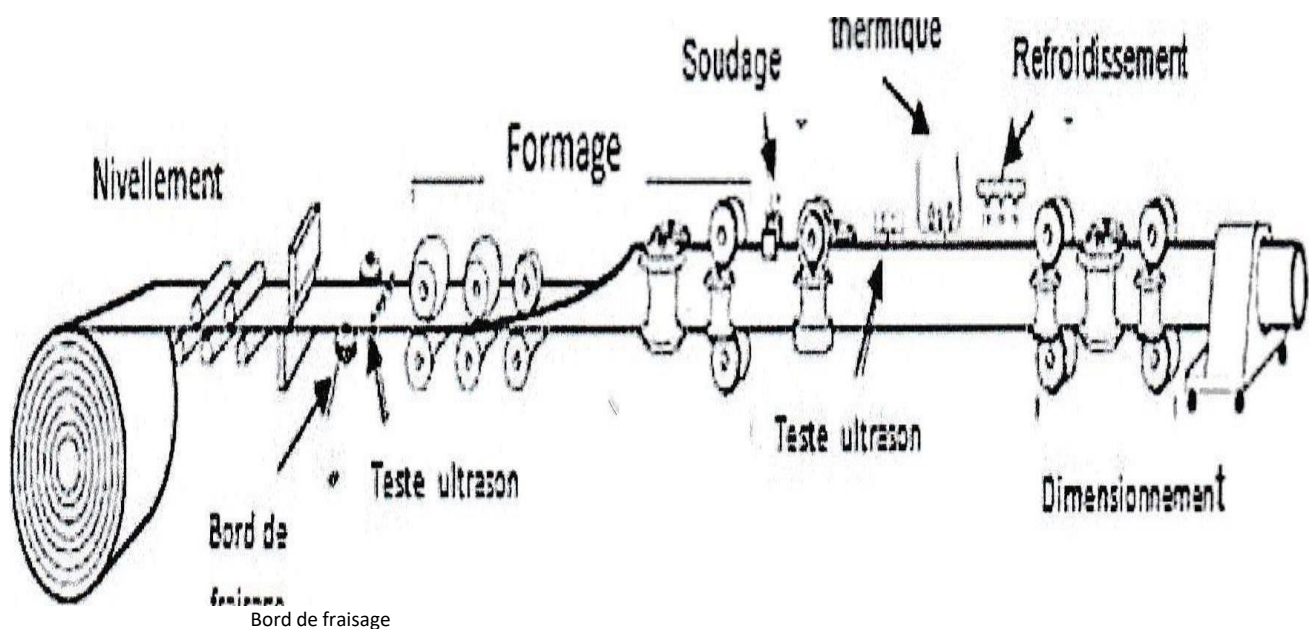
Technique de fabrication des tubes soudés en spirale
